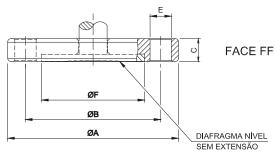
(d) – Diseño Dimensional de Montaje del LD291 – Nivel
